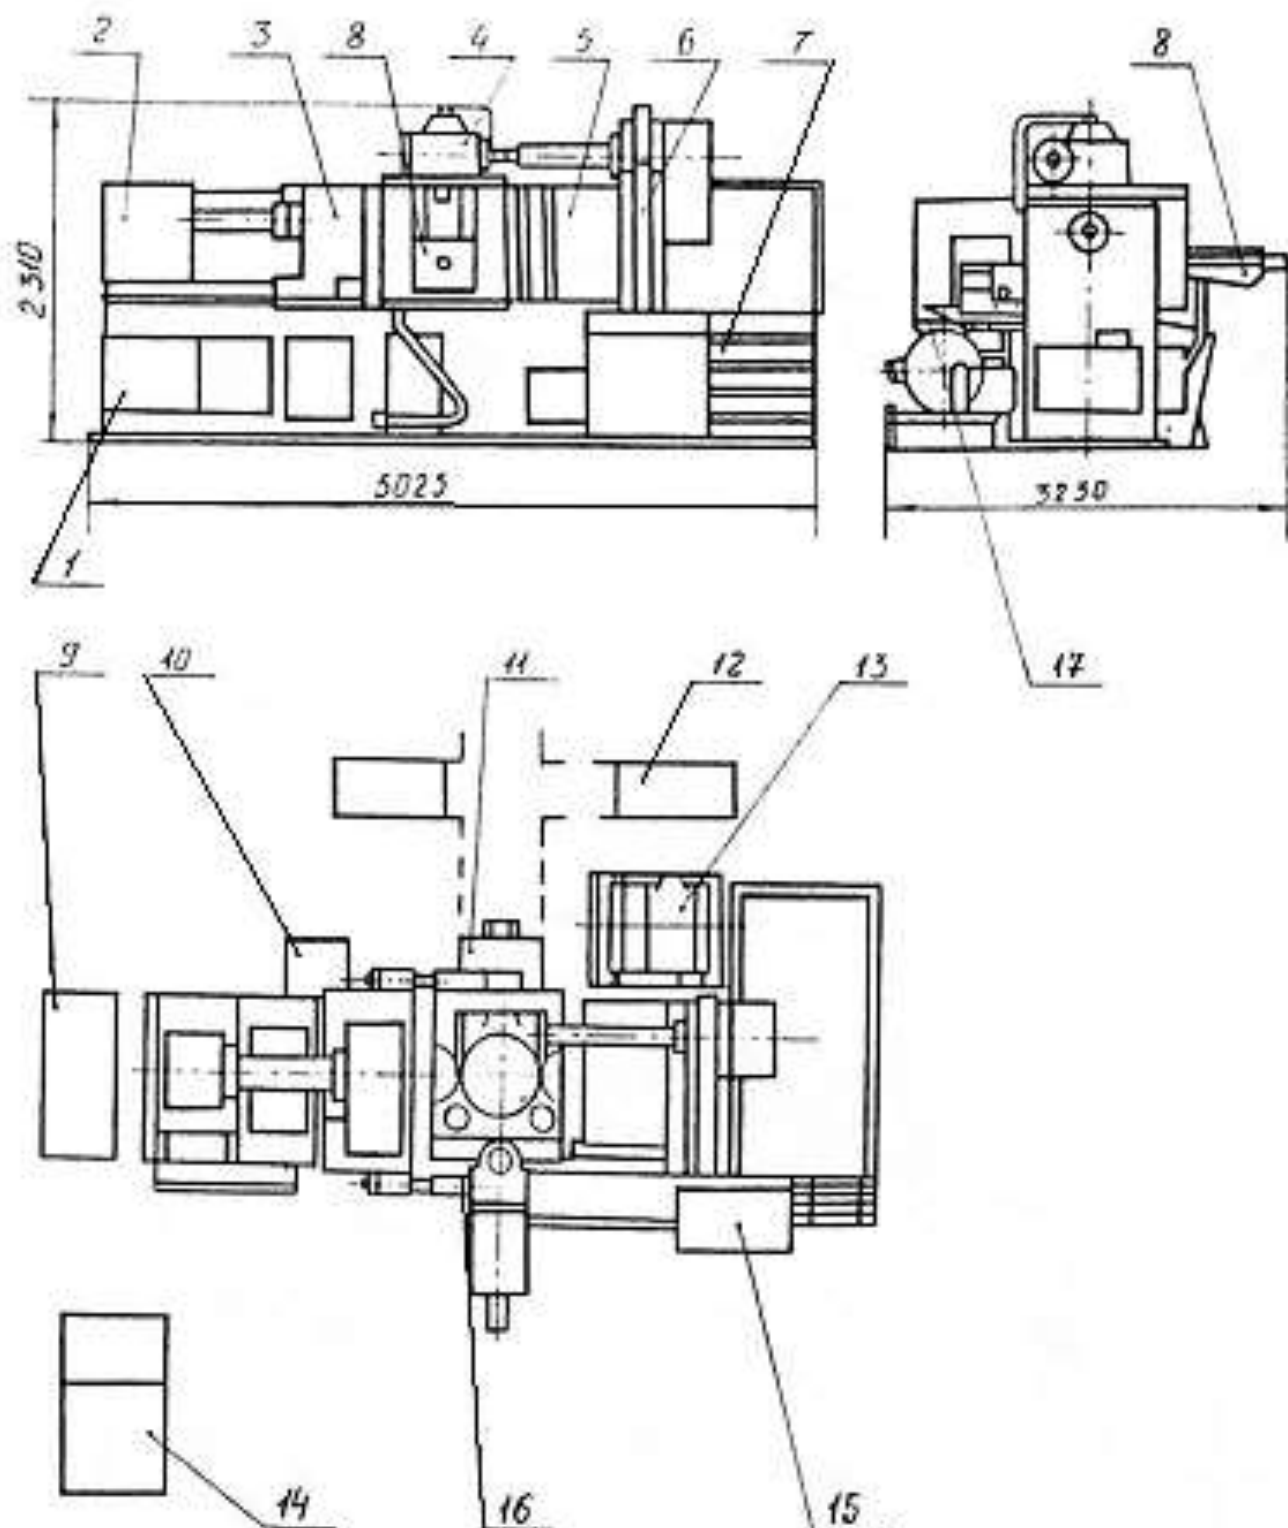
Рисунок I - Схема зубопроркатного стану ЗІС - 250
